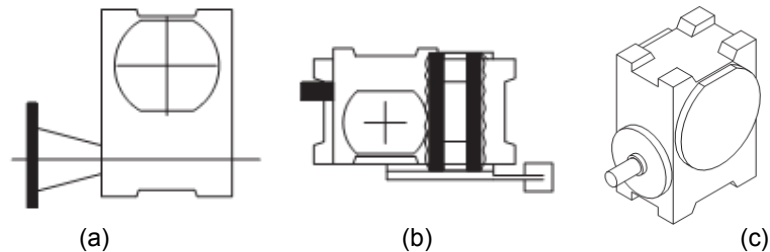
Entrada da ponta de eixo do MIT com flange tipo lanterna (a), braço torção (b) e posição de trabalho (c).
